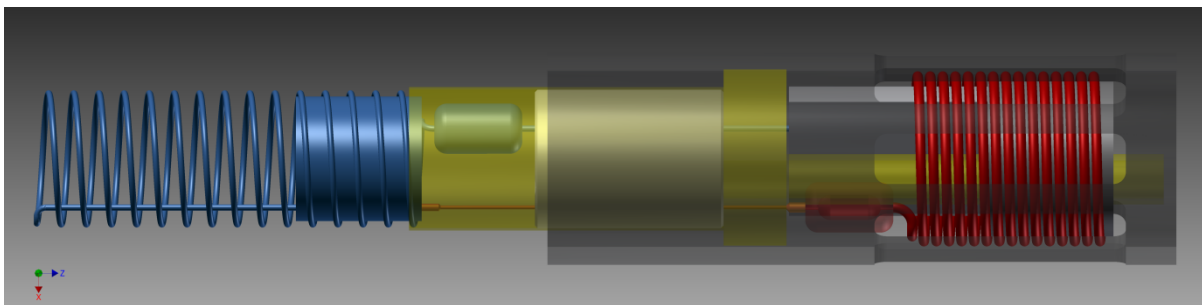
CAD-Entwurf einer Bohrloch-Kältemaschine
